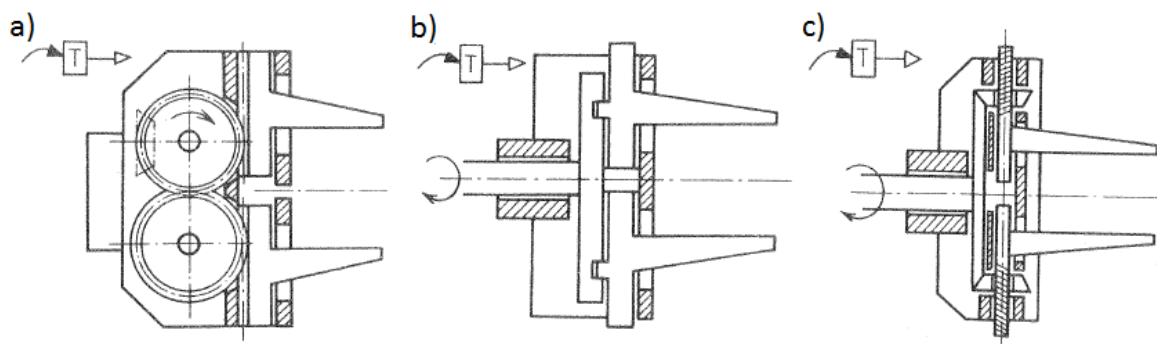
Kinematické uspořádání úchopných hlavic s rotačním motorem a otočnými čelistmi [34]
